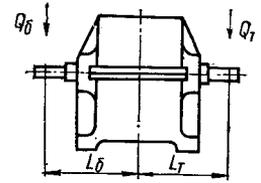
Приложение консольных нагрузок на валы редукторов ЦДН:
